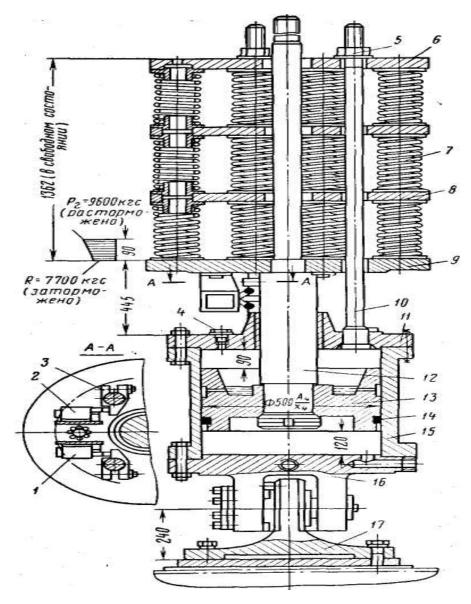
Пружинно пневматический безгрузовой привод тормоза крупных подъемных машин
